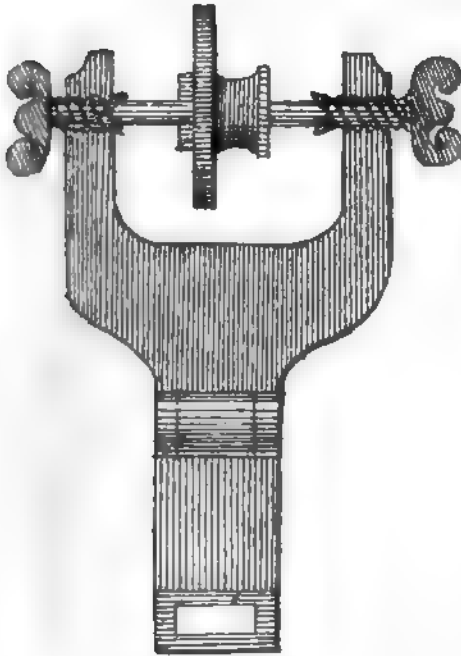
Fräser für Zahnräder, nach Leupold, 1794. (Vgl. die Abbildung Teilmaschine).
